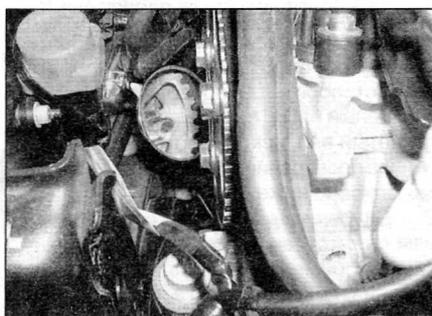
, а. Используйте зеркало для наблюдения за установочным пазом в ступице зубчатого шкива распределительного вала (двигатели 2.0 л)
